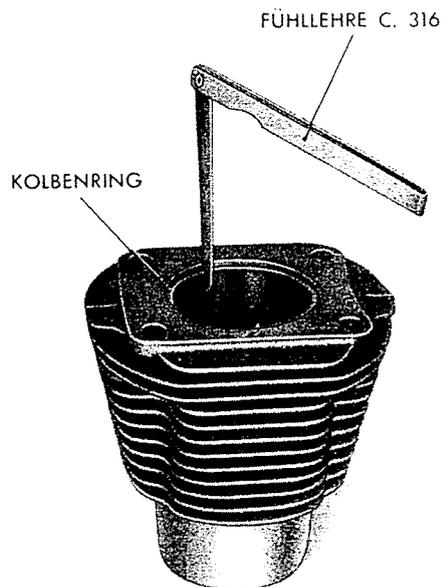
Kolbenringstoss mit Fühllehre prüfen.
